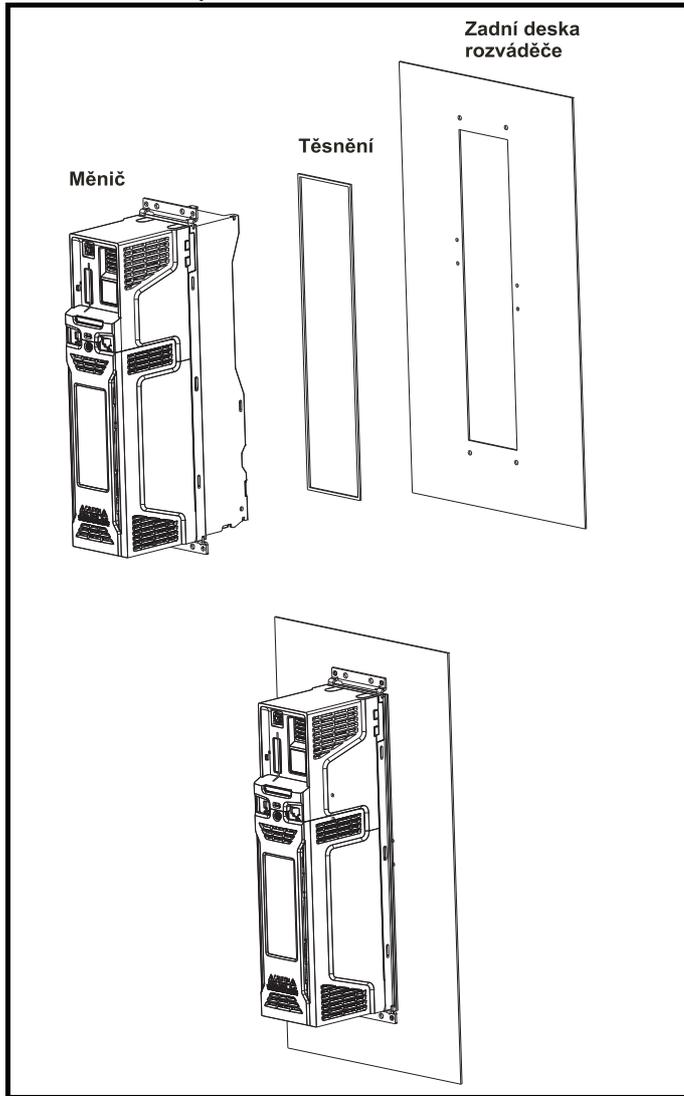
Příklad provedení IP65 (montáž skrz díru v panelu)
